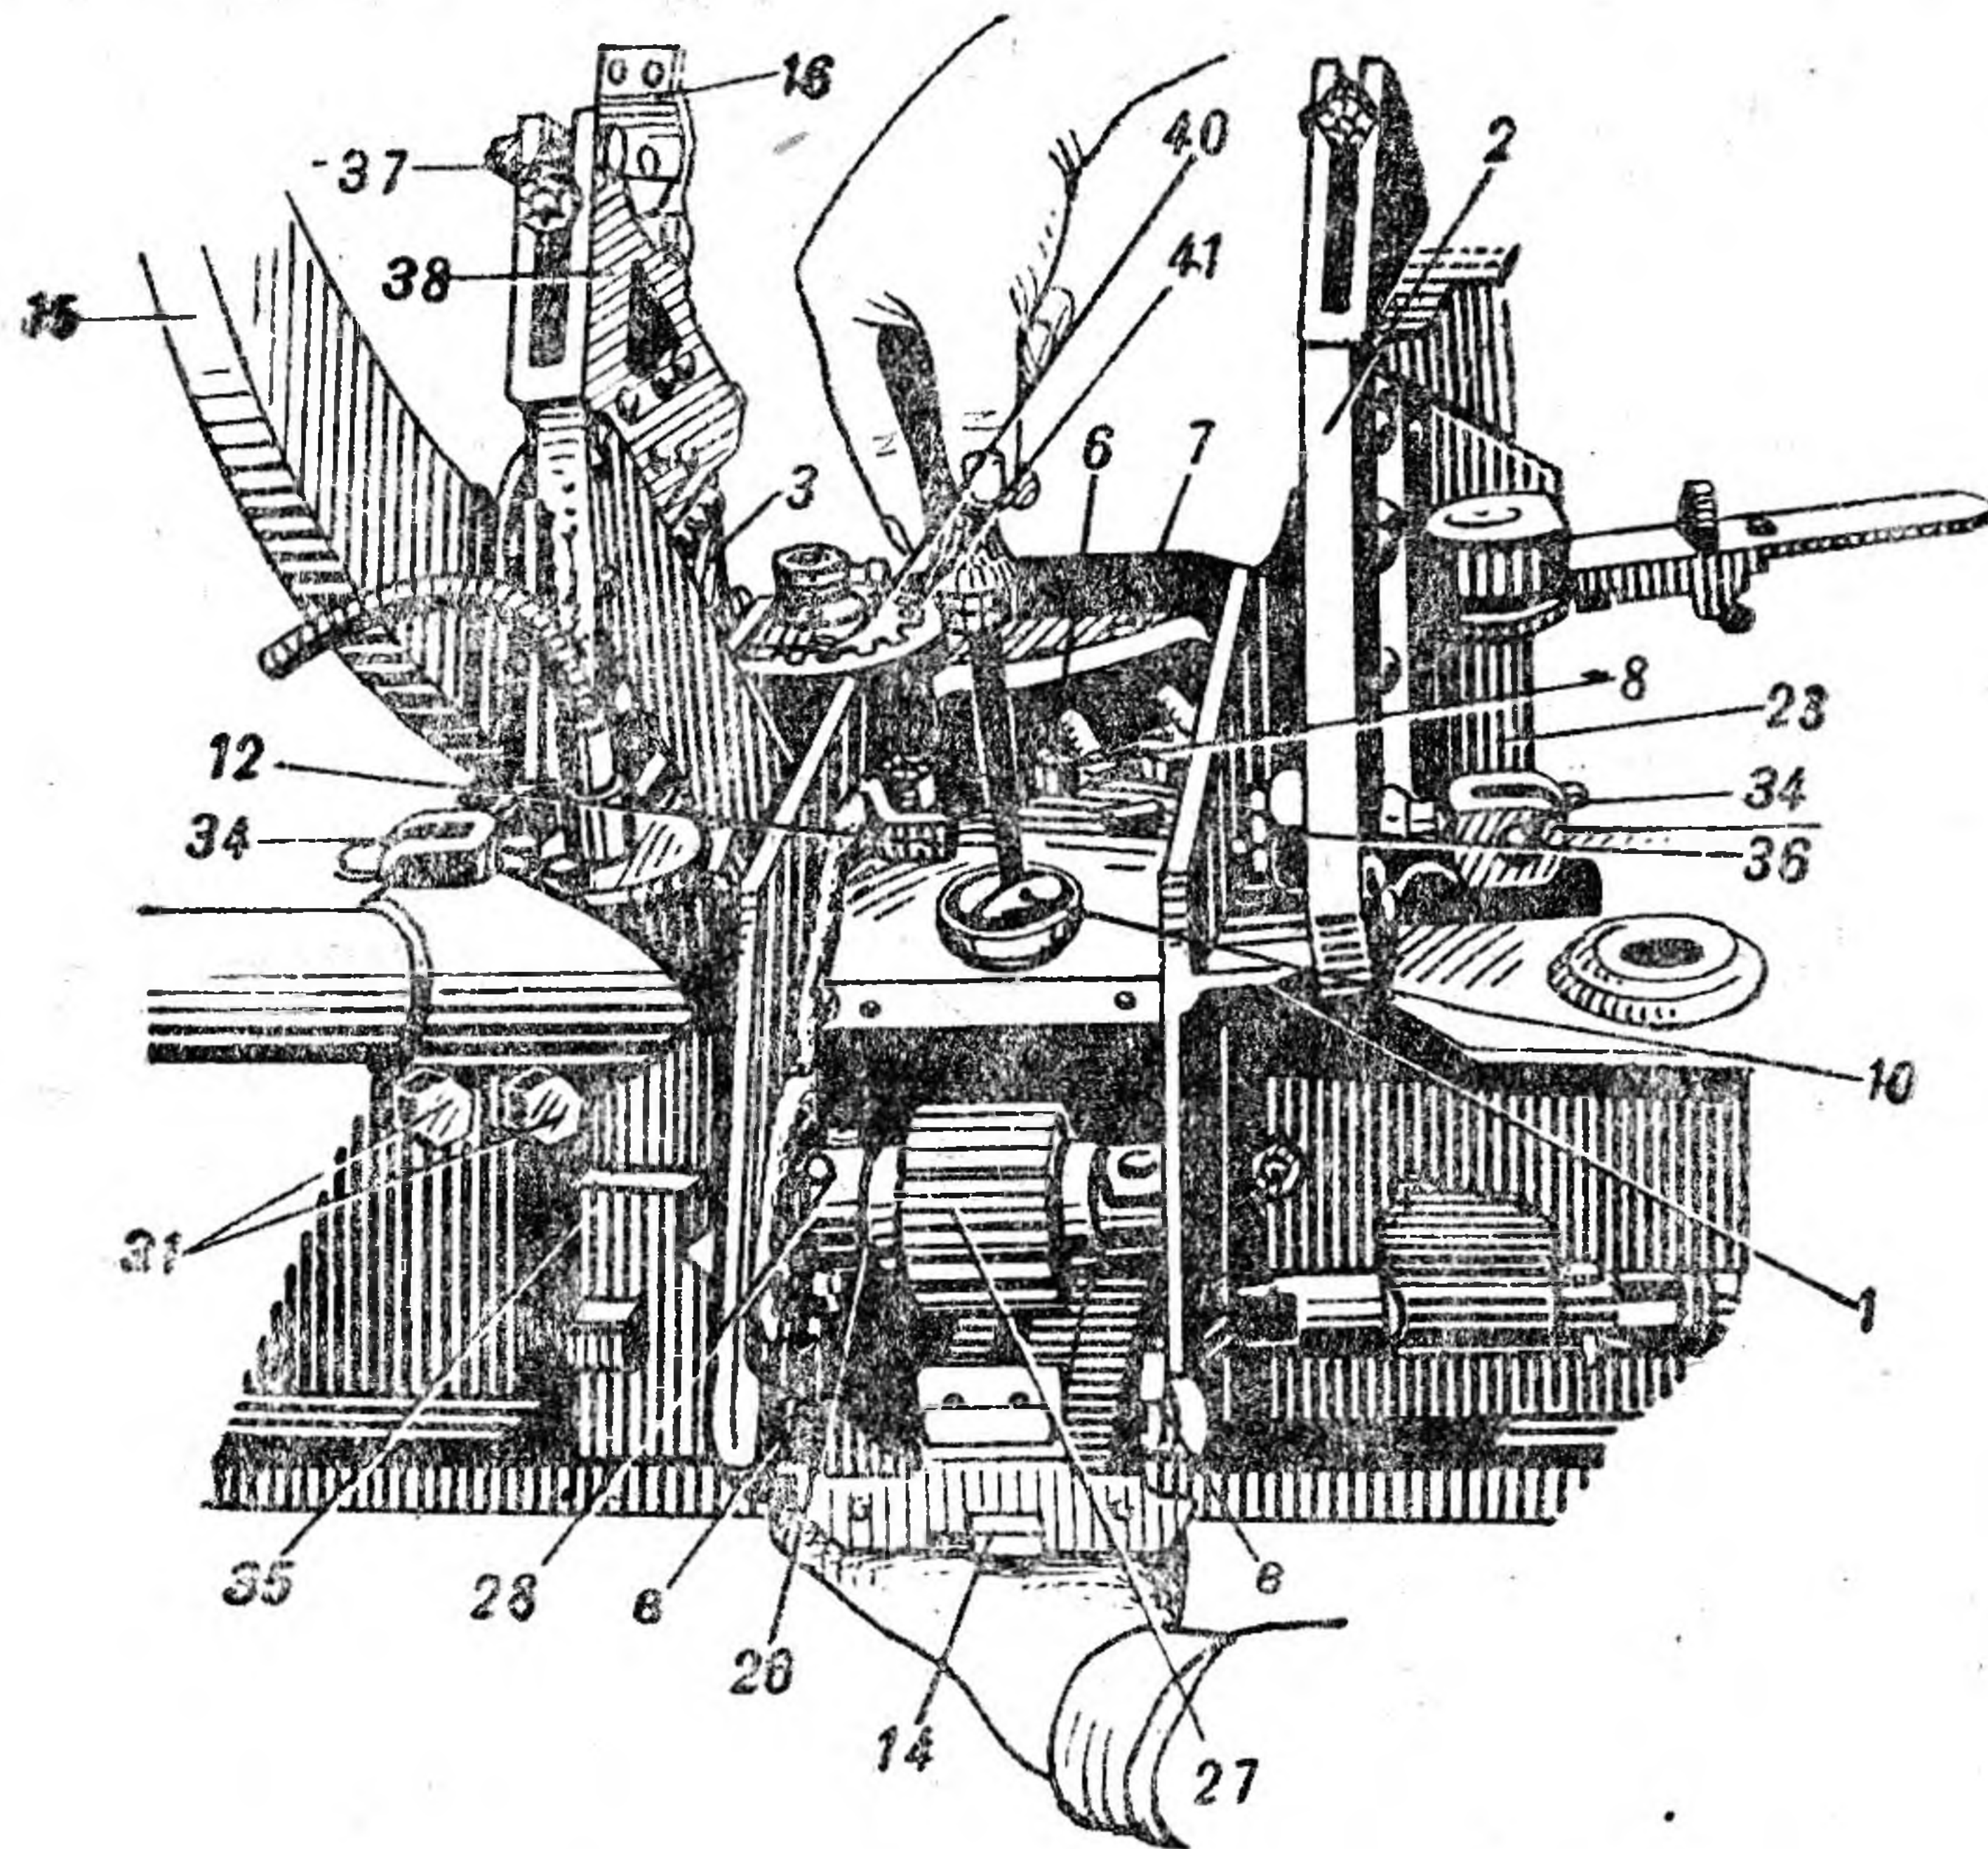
Верхний станок на нижнем станке (вид сзади)
